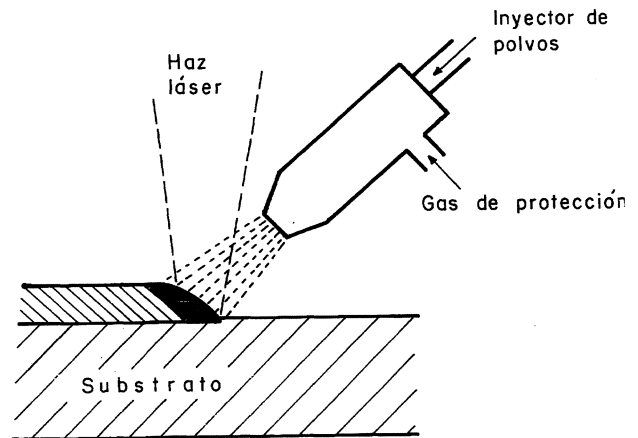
Esquema del montaje experimental para el plaqueo con láser mediante la técnica de inyección de partículas.
